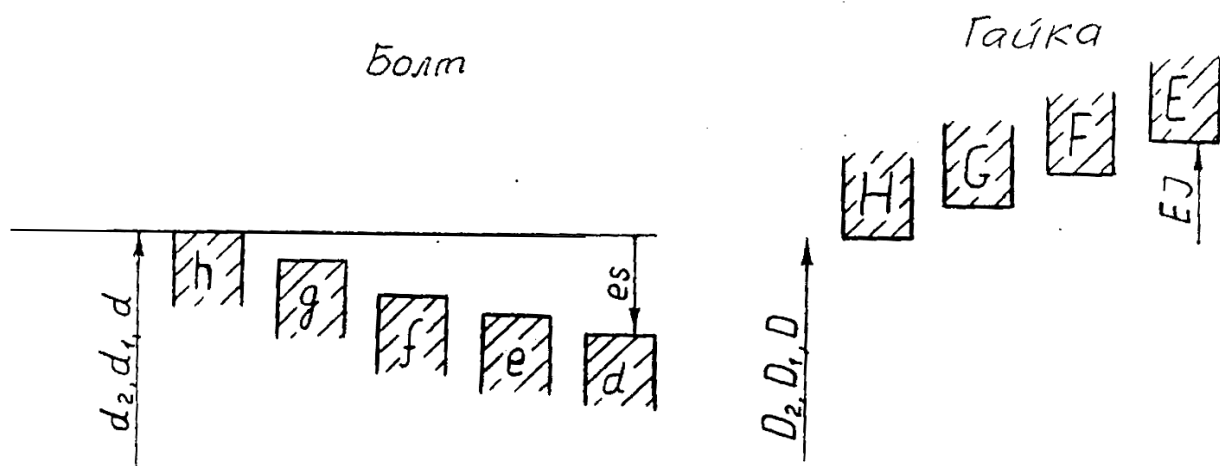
Схема расположения полей допусков резьбовых деталей с зазором
